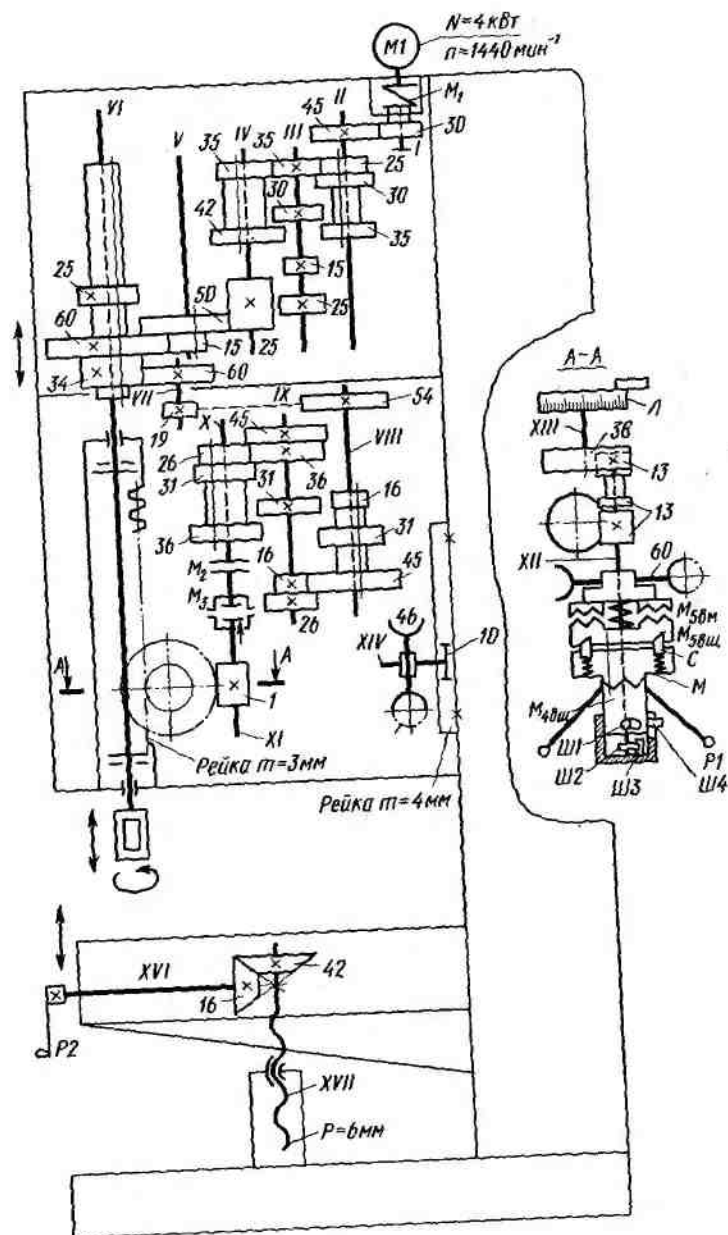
Кинематическая схема станка мод. 2Н135
